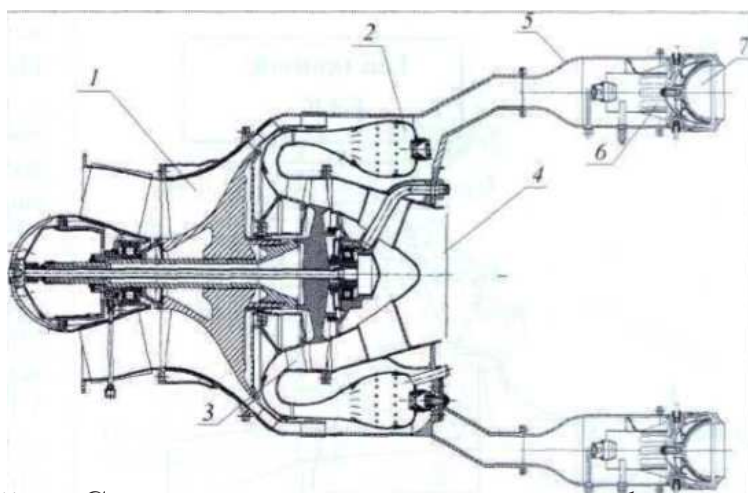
Схемно-конструкторская проработка исследуемого ПуДД для БПЛА: 1 - компрессор; 2 - камера сгорания; 3 - газовая турбина; 4 - реактивное сопло; 5 - тяговый модуль; 6 - реактор; 7 - резонатор
